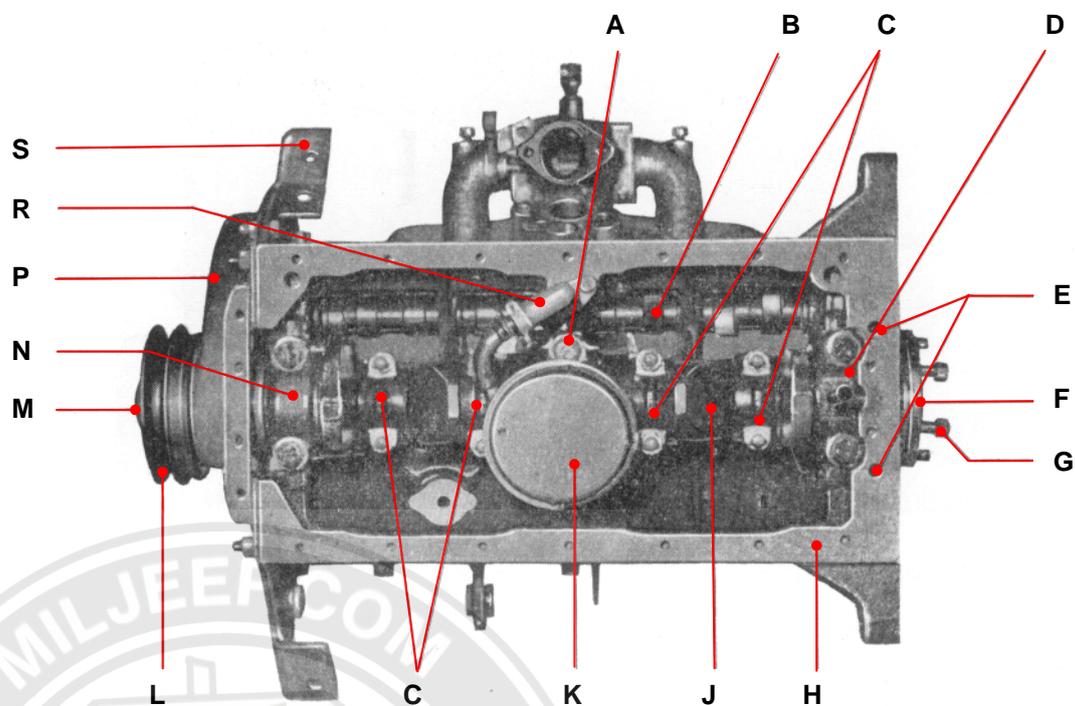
Vue de dessous du moteur, la cuvette d'huile étant déposée.
